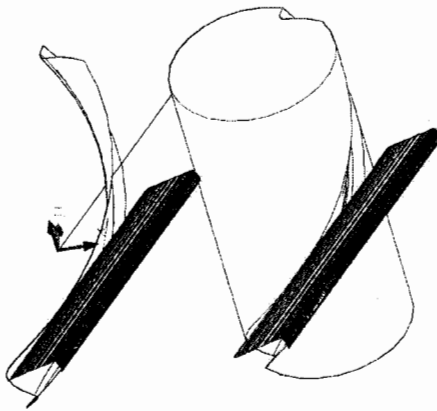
Модели цилиндрической и винтовой сопряженных поверхностей
